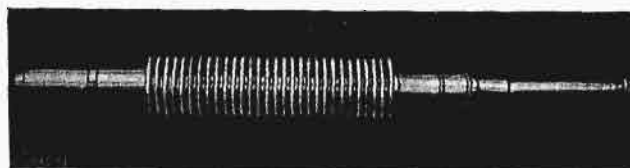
4-kadłubowa turbina I-szej Brneńskiej Fabr. Maszyn dla kopalni Witkowiec.
